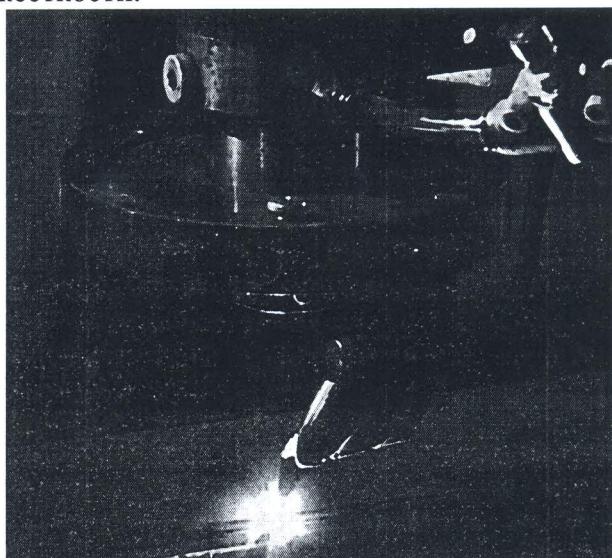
Процесс лазерной сварки Al-Li сплава 3 поколения (ИТПМ СО РАН).
